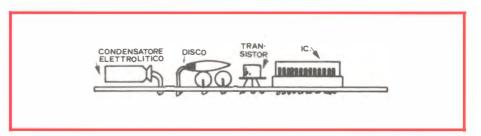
Basetta stampata tipo a montaggio ultimato e vista in sezione: notare i componenti piegati, anche su altri, per contenere l'altezza del montaggio.
